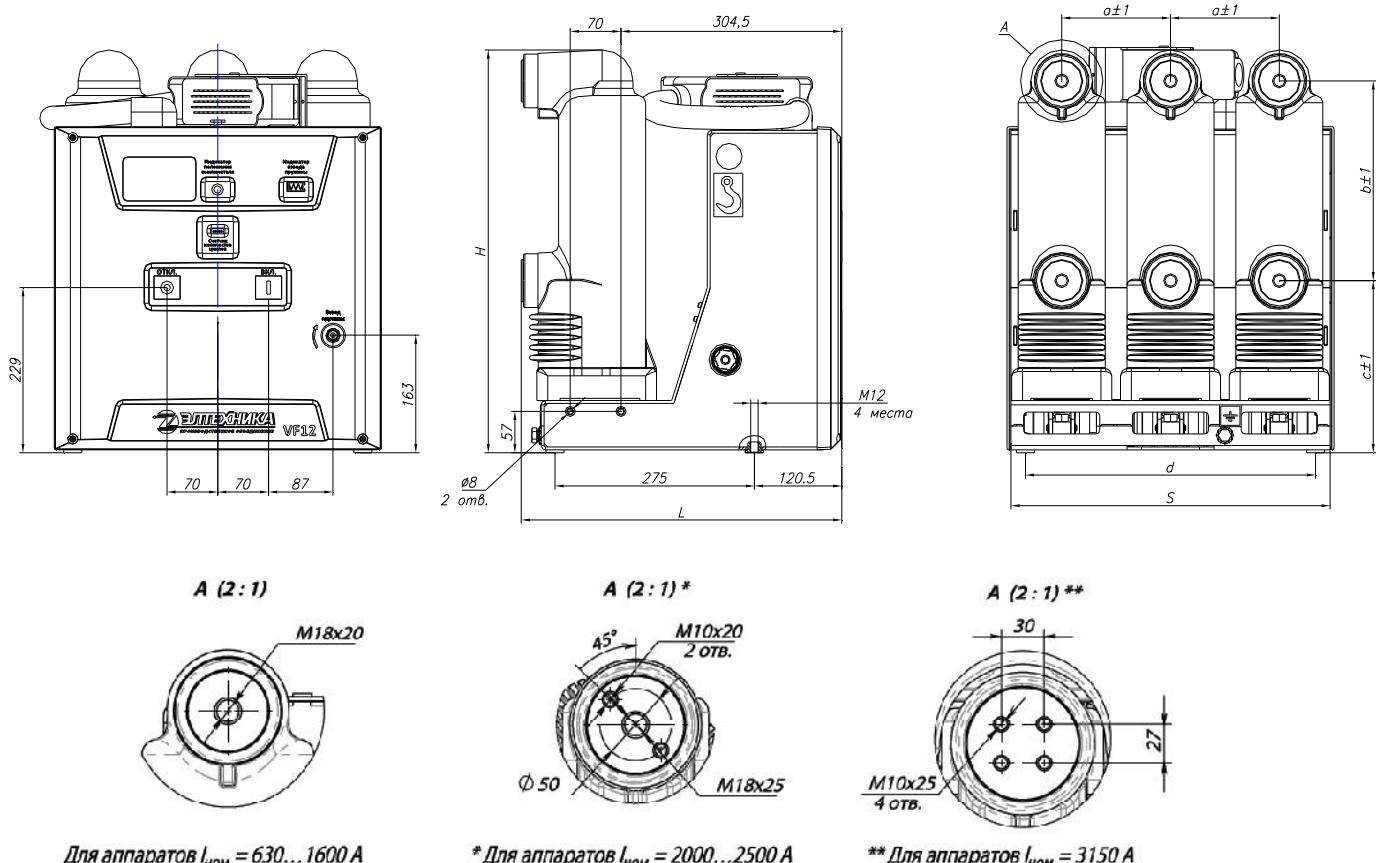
Габаритно-присоединительные размеры выключателей в исполнении S без обрамления.
